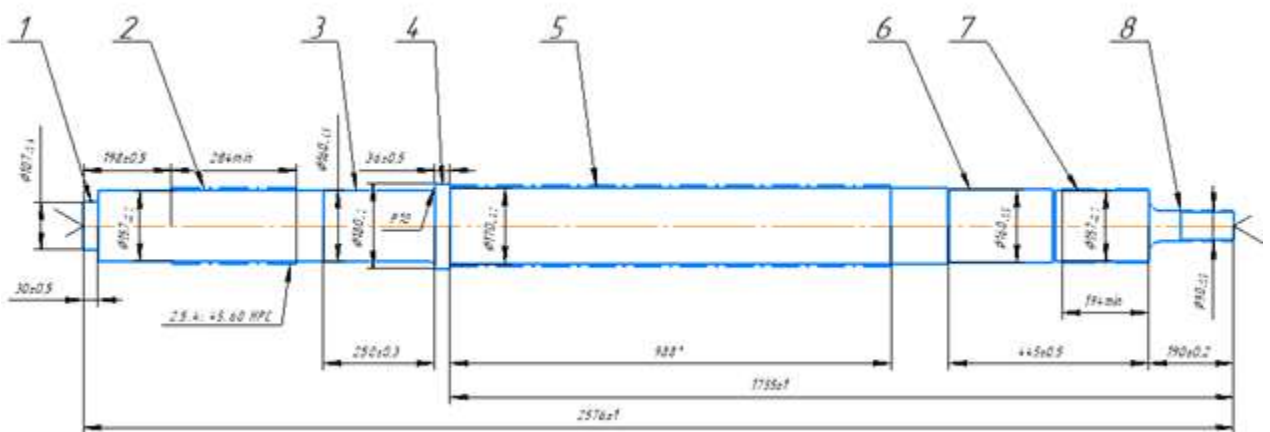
Обозначение поверхностей заготовки вала под закалку
